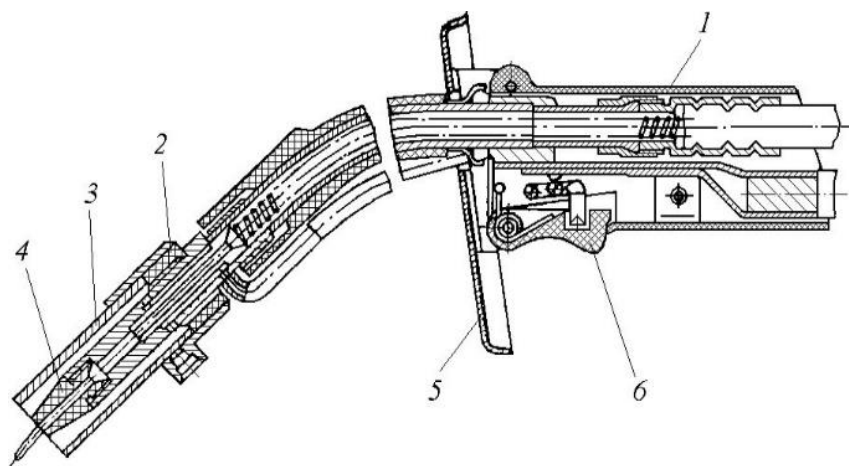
Горелка шлангового полуавтомата для сварки в защитных газах
